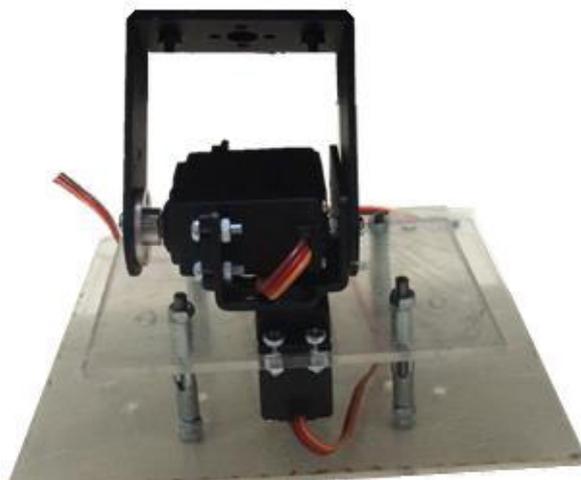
ENSAMBLE DE PLACAS BASESERVO Y TAPA CUERPOB
